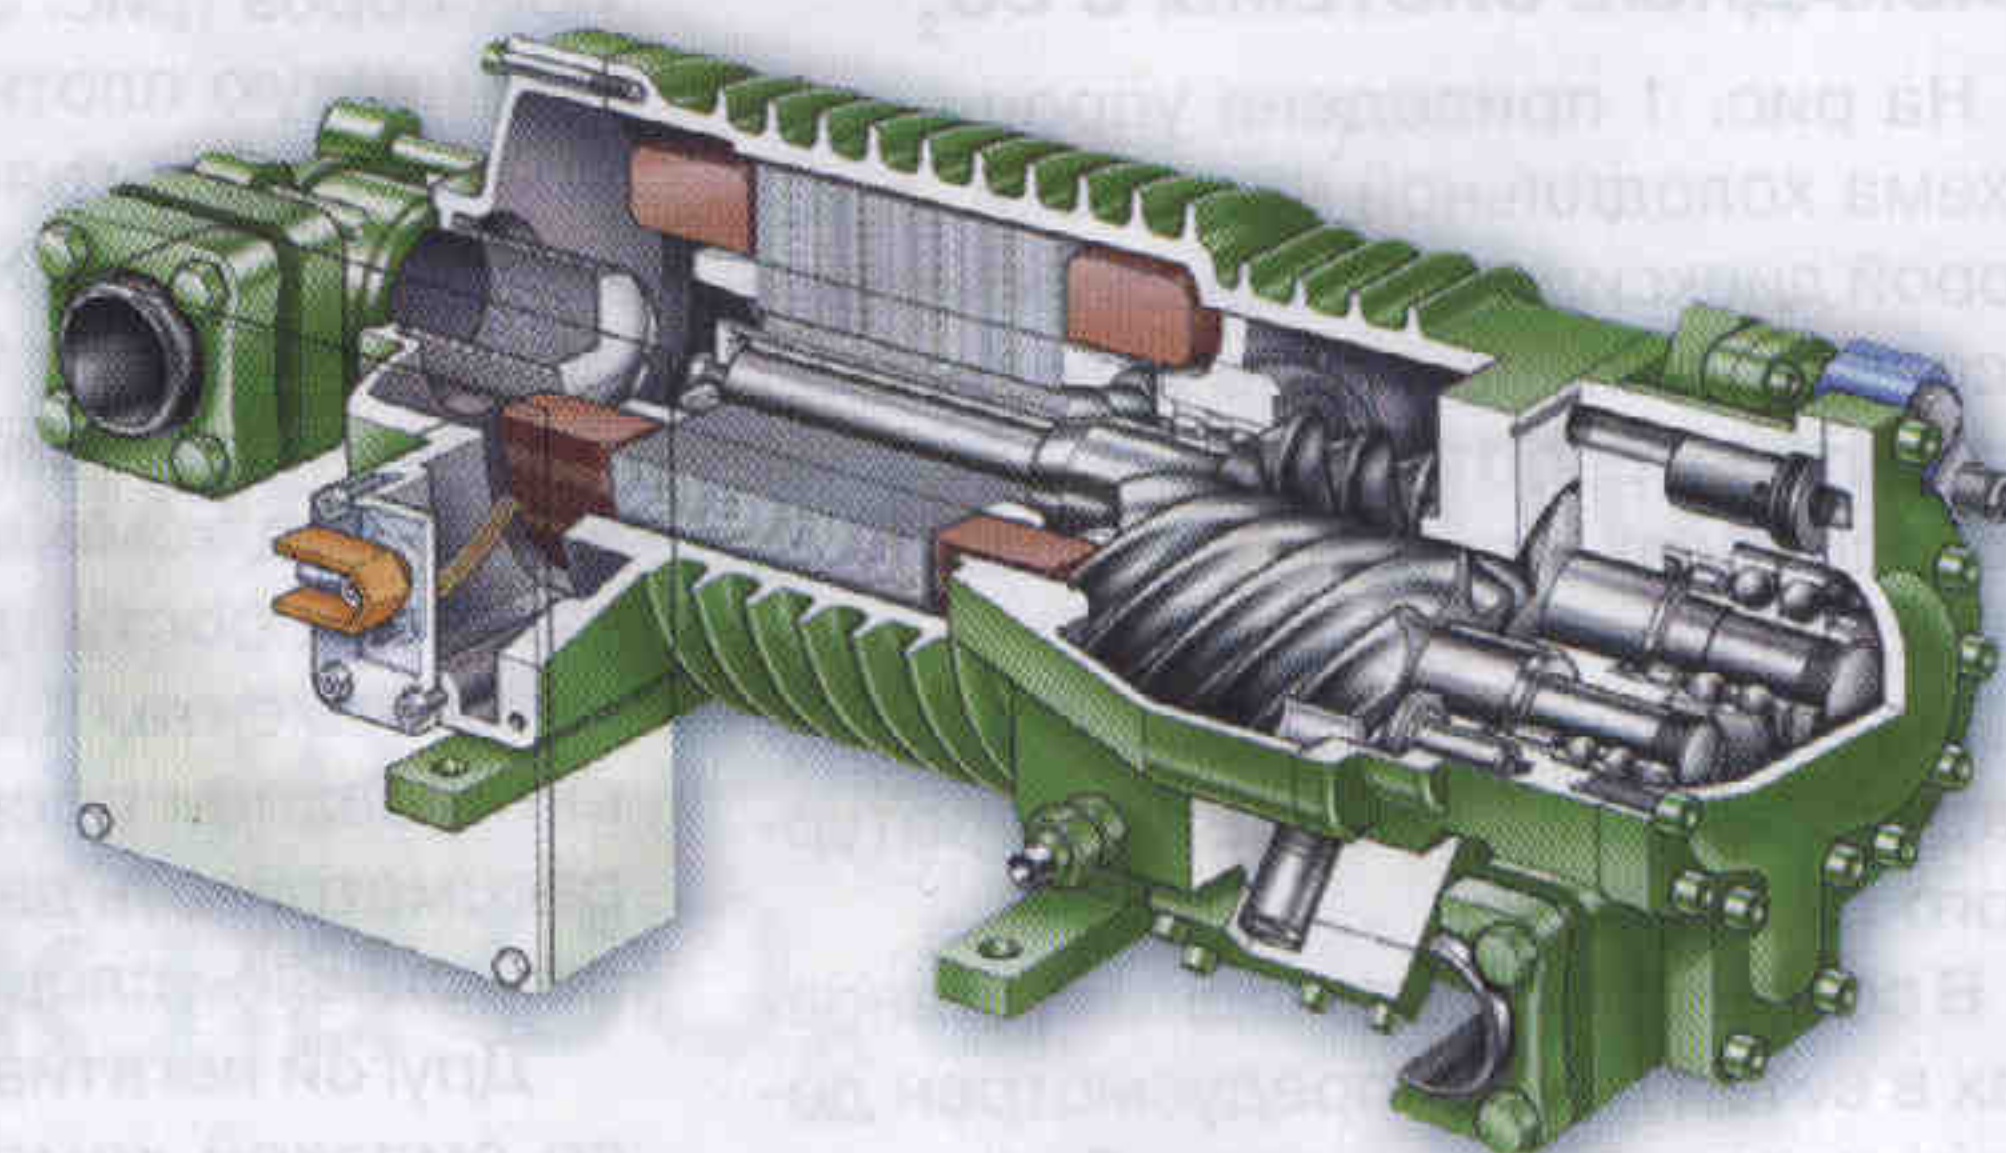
Разрез полугерметичного винтового компрессора (без маслоотделителя)
